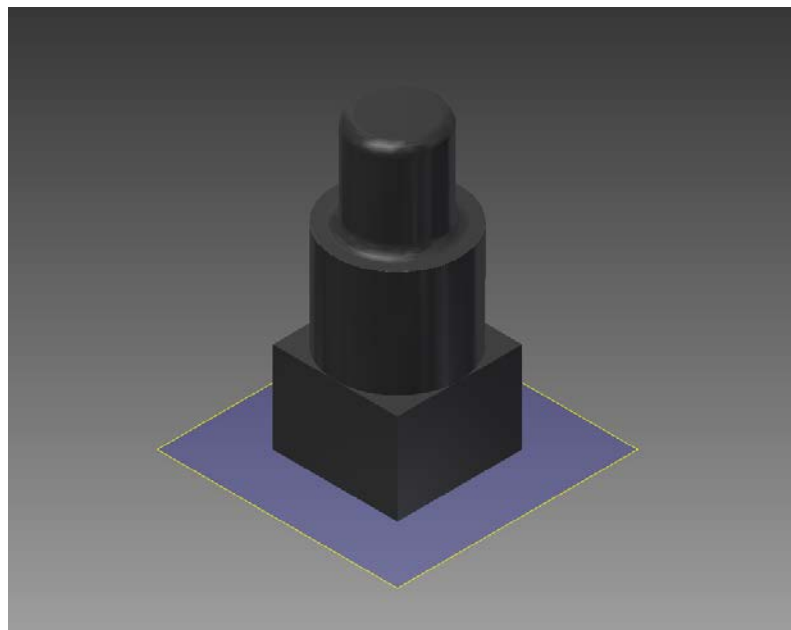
Parte del eje de salida que se inserta en el quinto engranaje.
